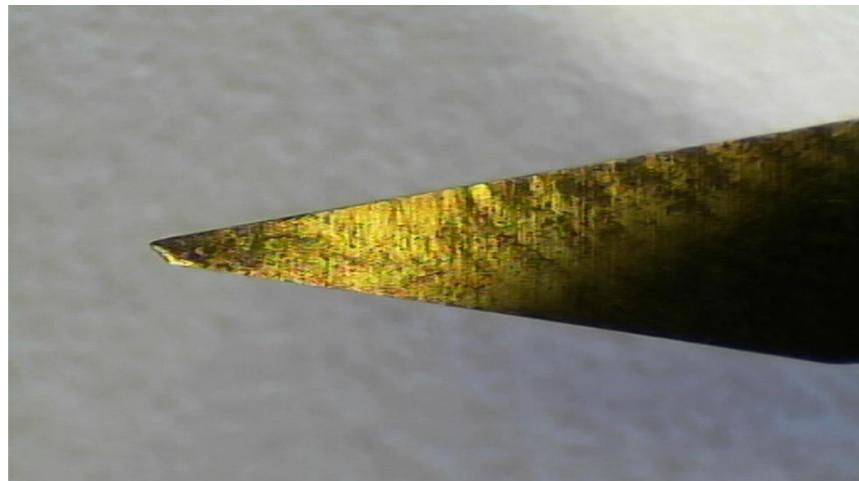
Desgaste en la punta de una fresa de carburo. Fuente: Bastián Urra Alcaino
